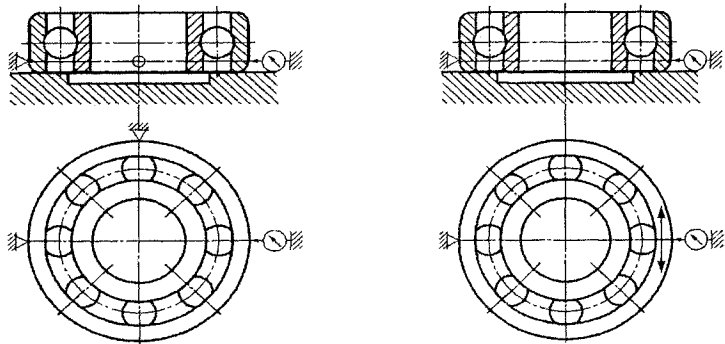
Схемы измерения посадочных размеров наружного кольца подшипника
